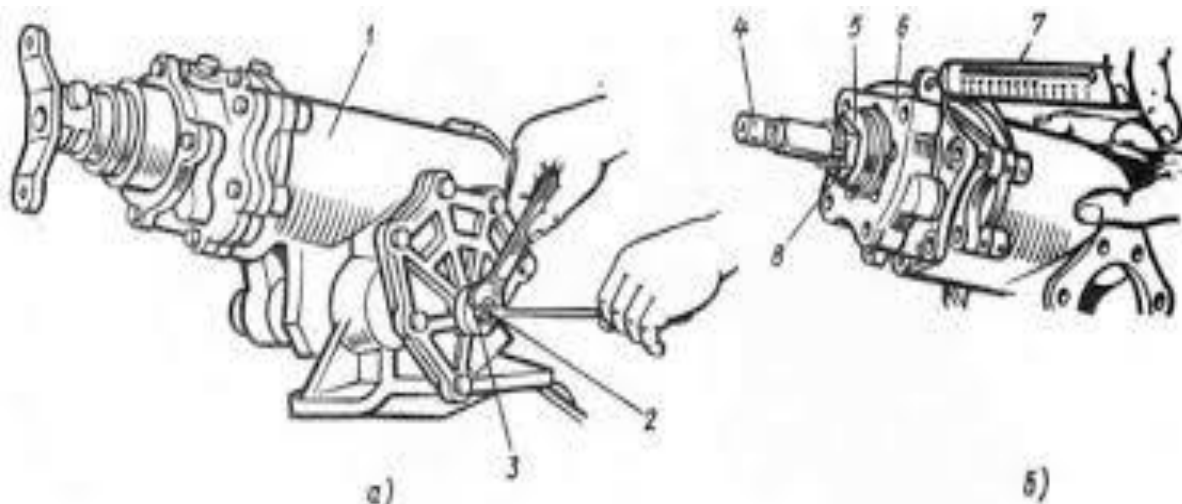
Регулировка рулевого механизма автомобиля ЗИЛ .
